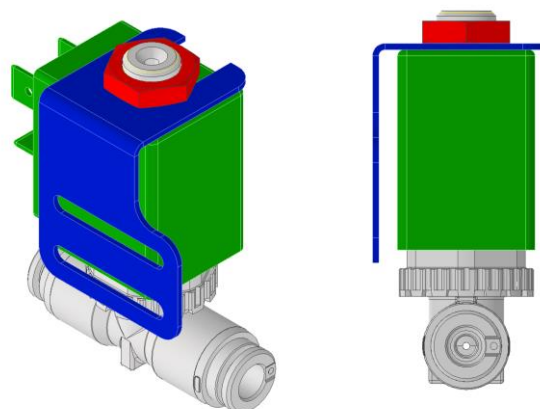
Magnetventil mit Befestigungsblech. Rot: Mutter, blau: Befestigungsblech, grün: Magnetspule, grau: Magnetventil
